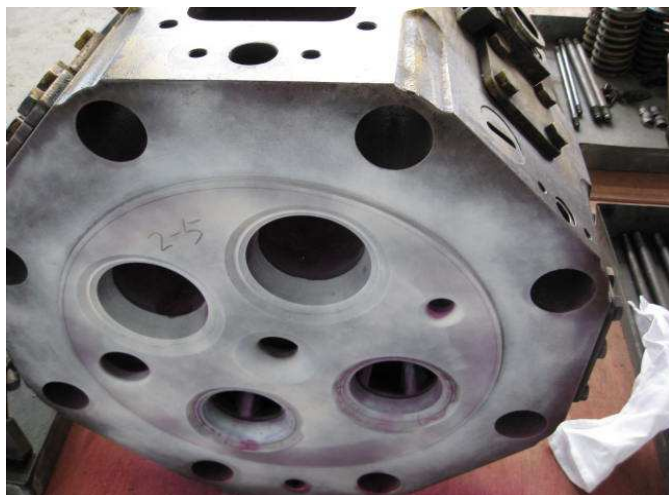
Цилиндровая крышка дизеля Sulzer ZL40/48
